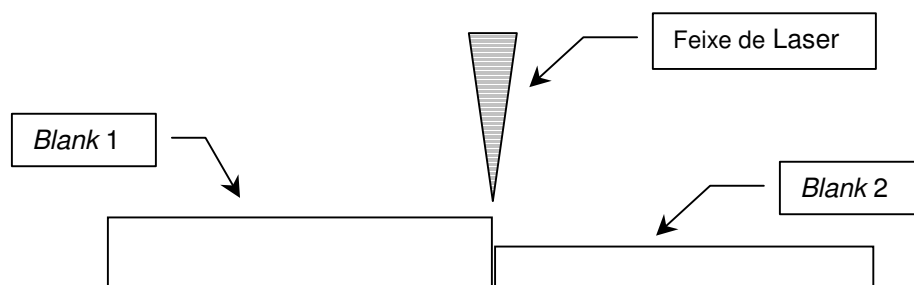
Blank posicionados sob o feixe Laser para serem soldados
